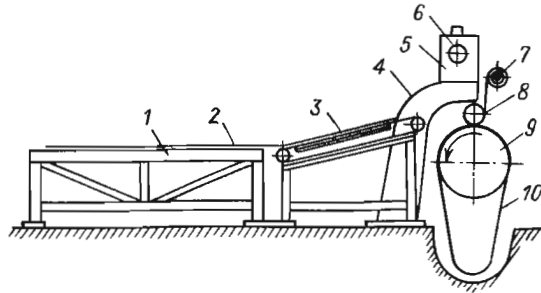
Схема станка для изготовления браслетов крупногабаритных покрышек: 1 — стыковочный стол; 2 — полотно корда; 3 — транспортер; 4 — станина станка; 5 — механизмы привода и центровки устройства для наложения резиновой прослойки; 6 — валик для закатки прослойки; 7 — рулон резиновой прослойки; 8 — прикатчик; 9 — барабан; 10 — браслет
